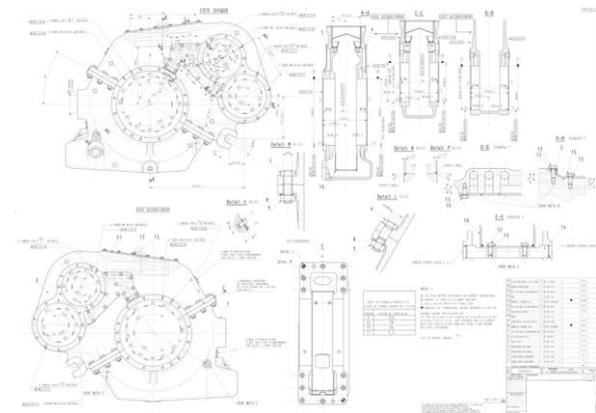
Desenho técnico de um cárter da caixa de transmissão de um rodado motor
